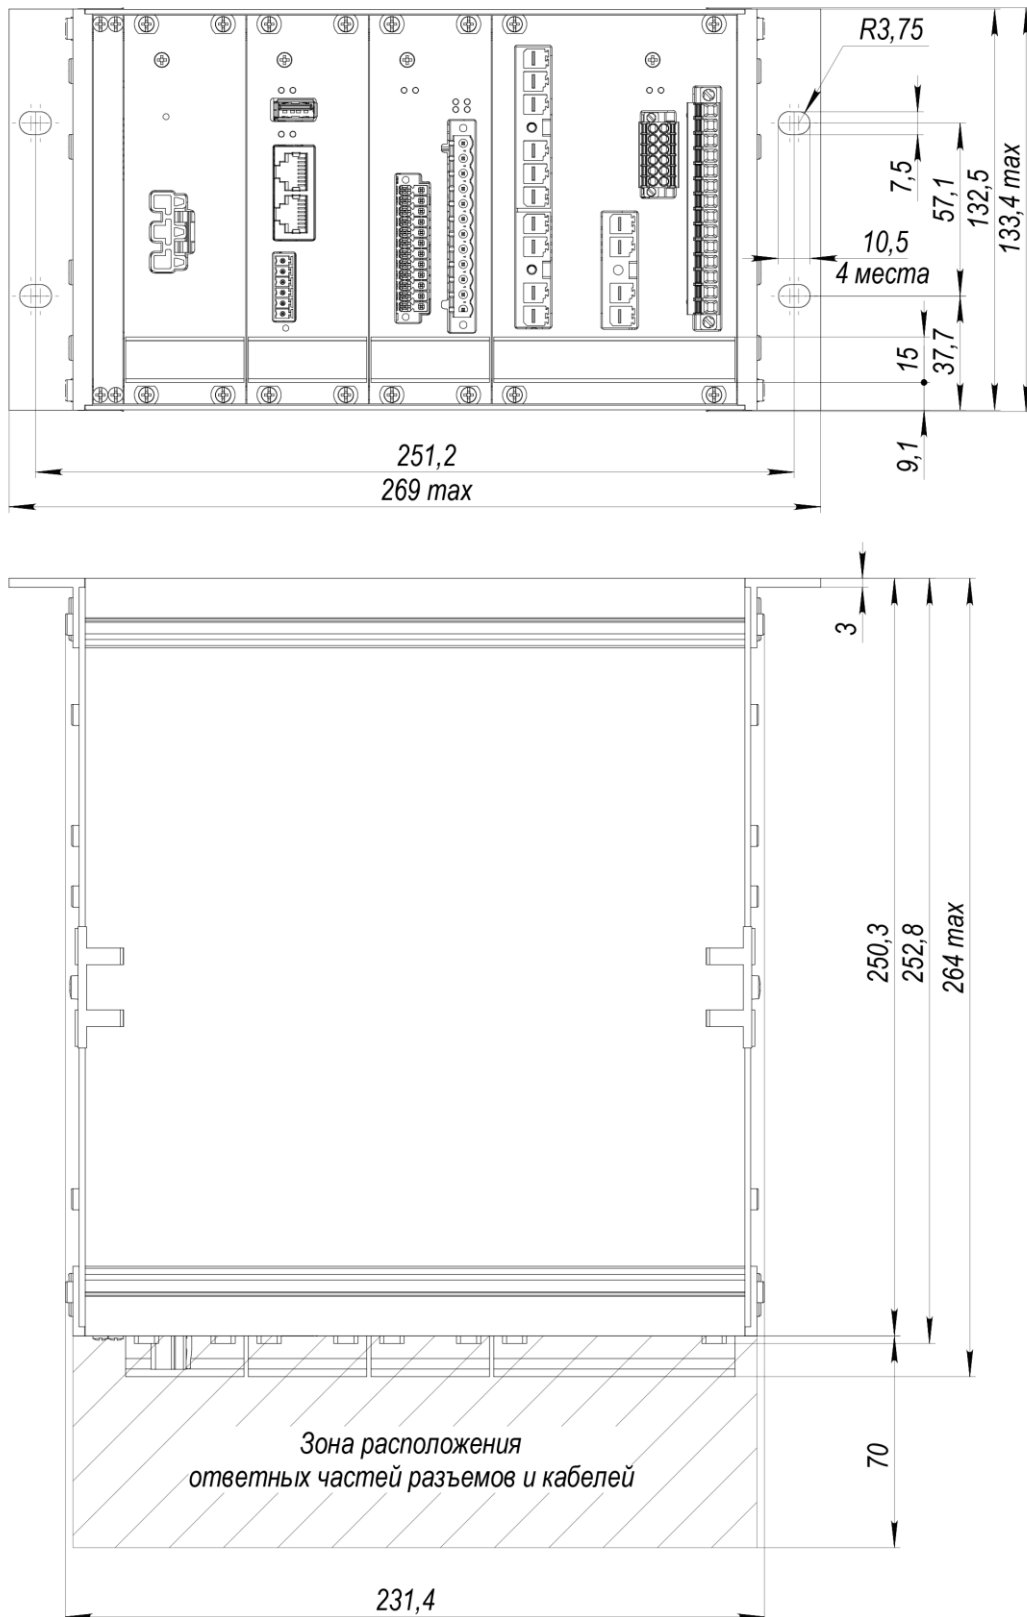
Установочные размеры контроллера АВ-ТУК-05
